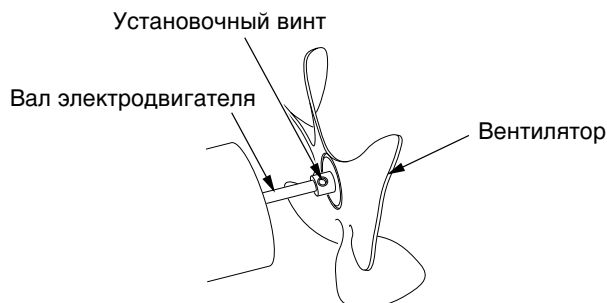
Расположение вентилятора, вала электродвигателя и установочного винта
